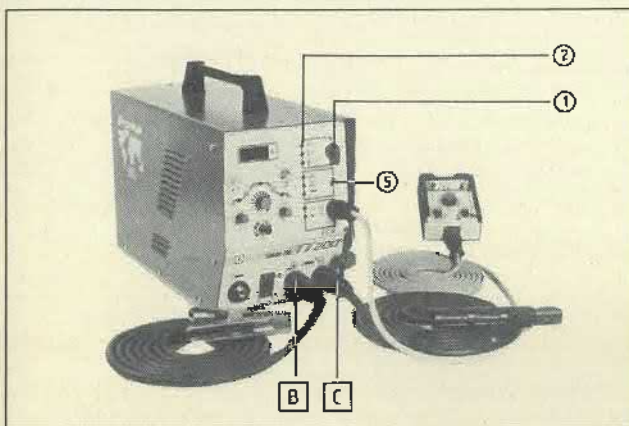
Transstig 200 als E-Handschweißgerät bestehend aus: Stromquelle, Handfernregler TP2 (wahlweise) und Schweißkabeln
